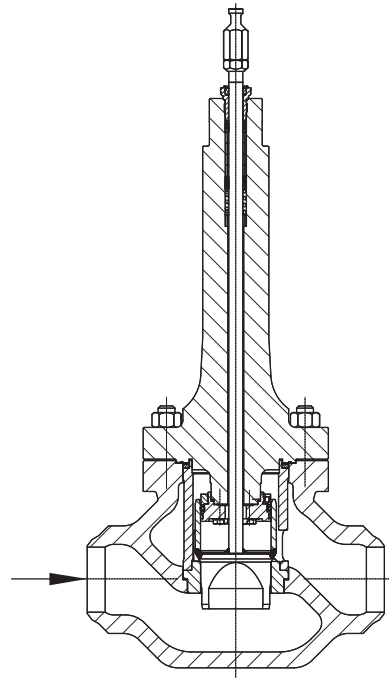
· Vanne type 3291 avec embouts à souder et pièce d'isolement
